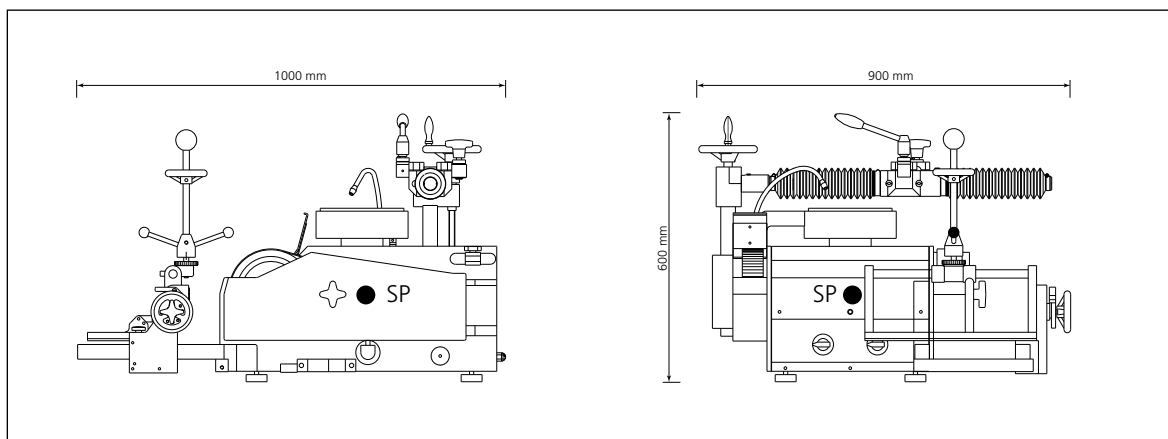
Dimensions en mm (S 200 T modèle table)
